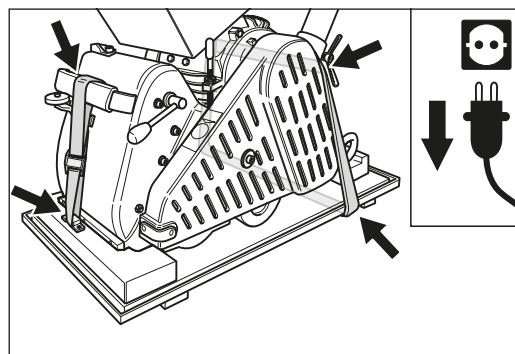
Transport ou entreposage de la machine sur le bas de la caisse de transport.
